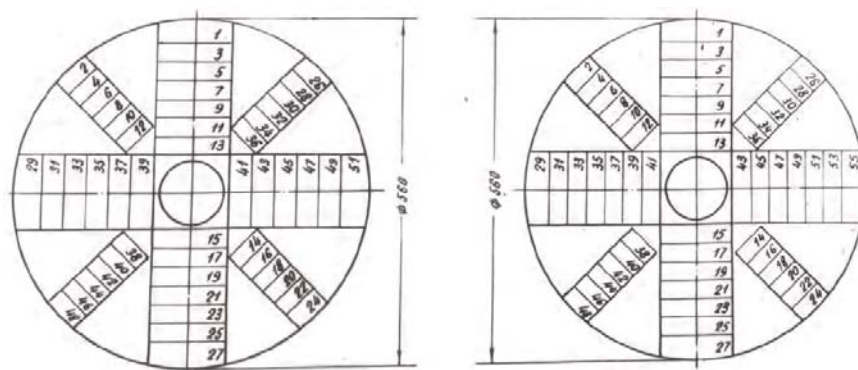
Схема вырезки образцов из диска заготовки роторного вала
